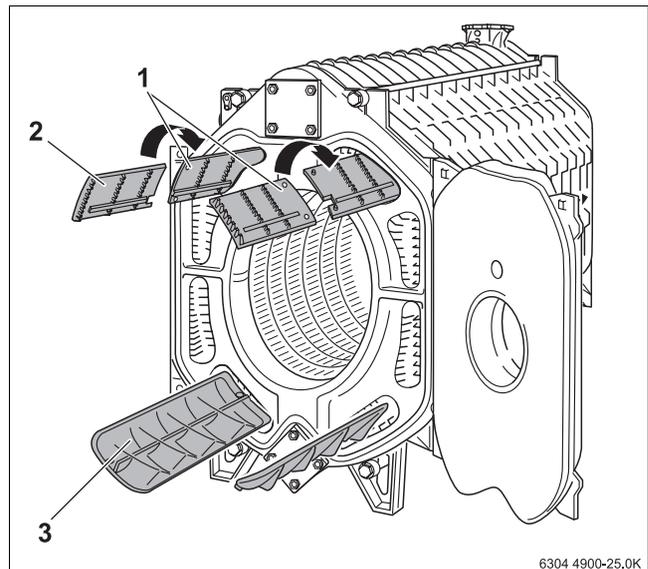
Heizgaslenkplatten einsetzen (Kesselblock mit 13 Gliedern)
